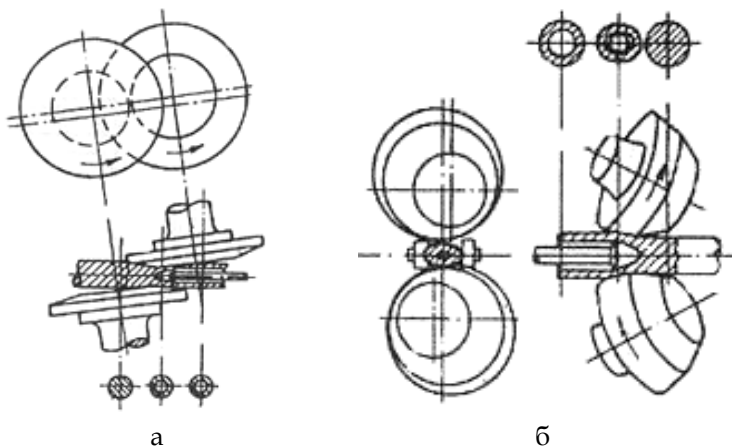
Схема прошивки на станах с дисковыми (а) и грибовидными (б) валками
